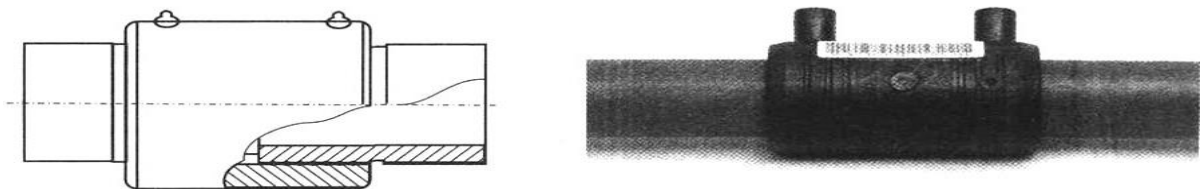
Качественно выполненное сварное соединение с ЗН
